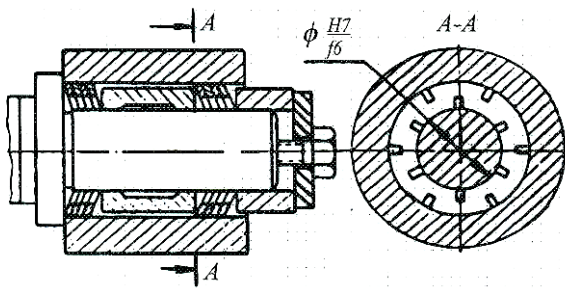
Установка заготовок на розтискній оправці з тарільчастими пружинами
